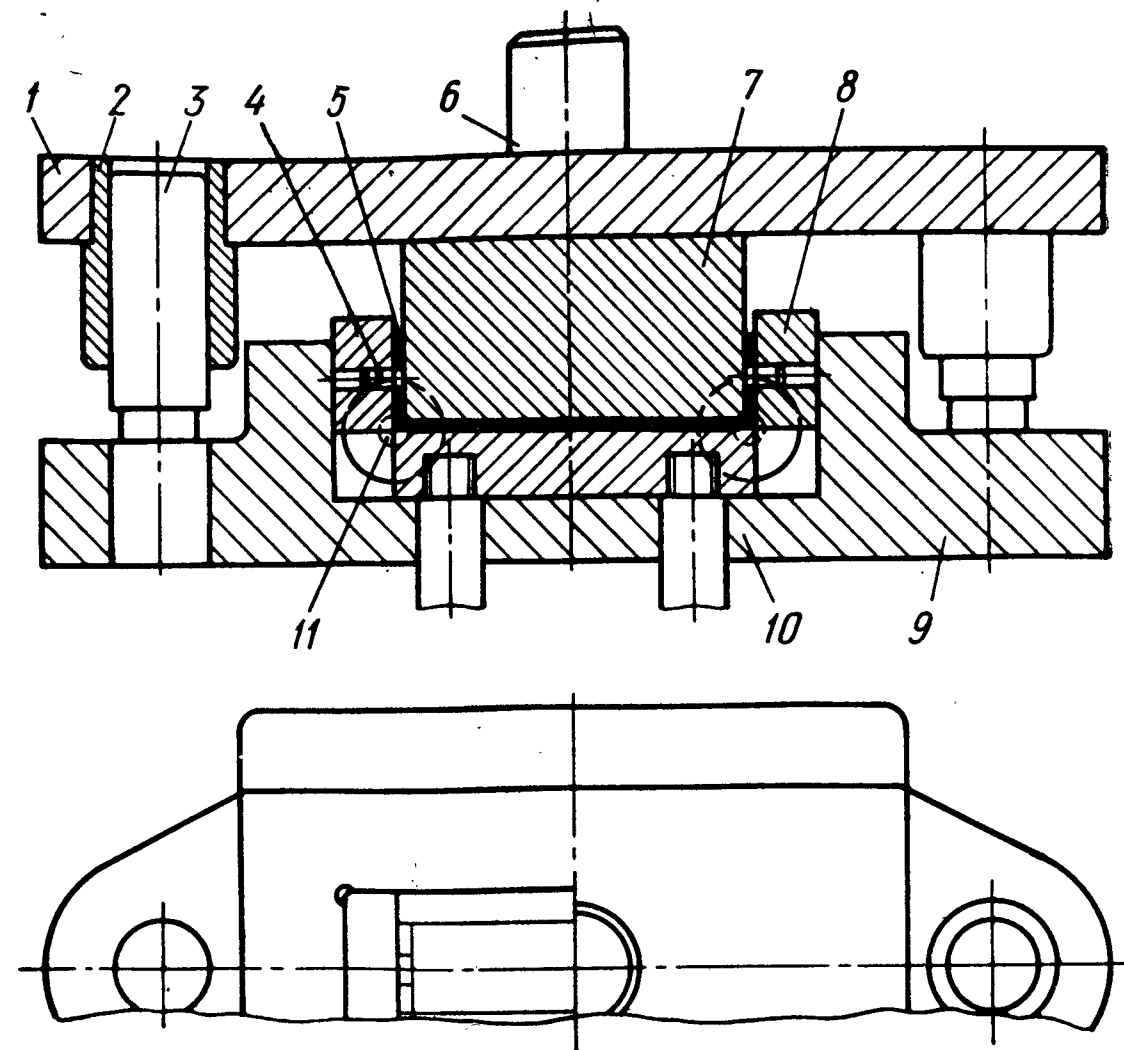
Штамп шарнирный для гибки скобы с отверстиями, расположенными на полках
